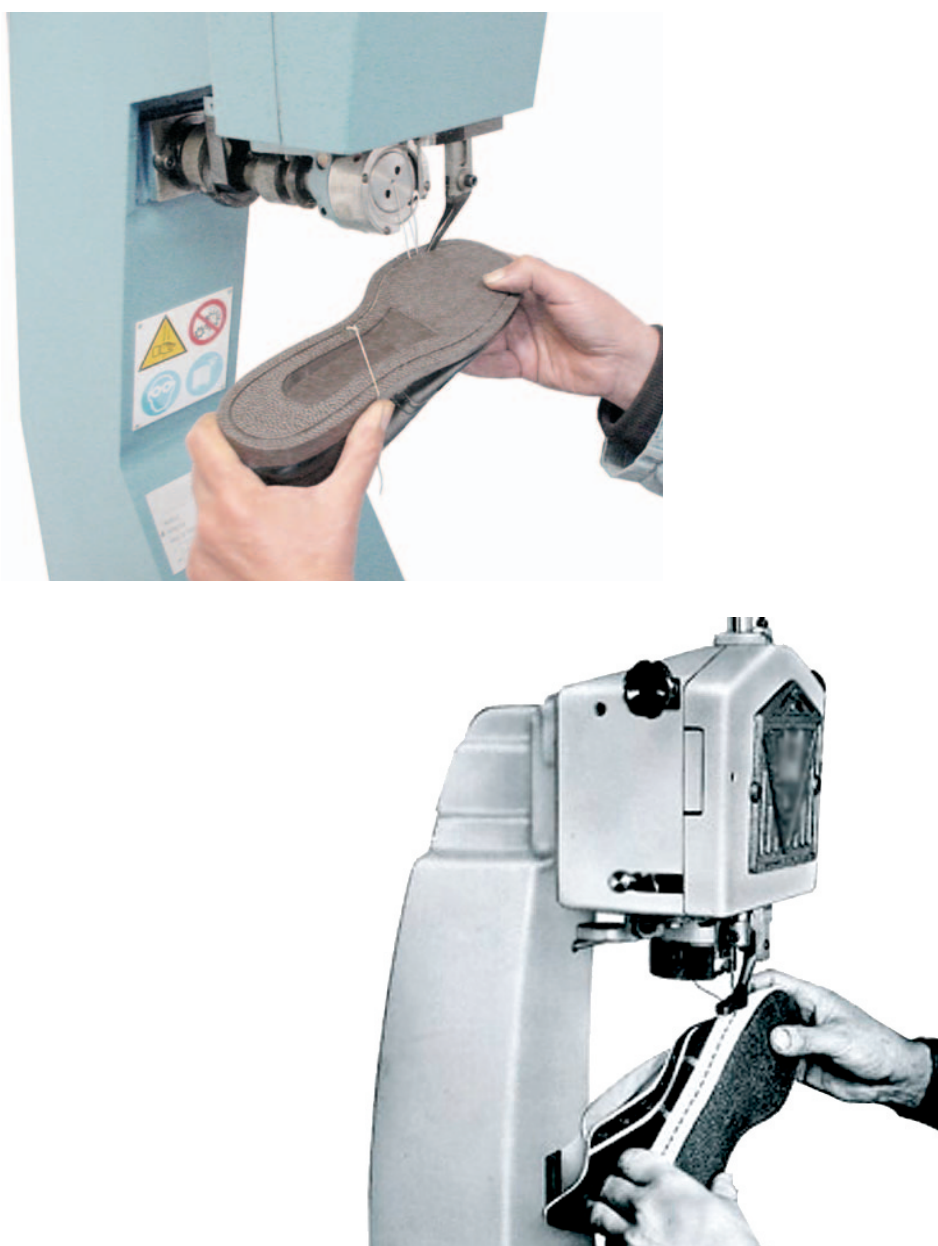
Exemple de machine pour la couture à Blake du fond de la chaussure sur la photo de gauche, et pour couture latérale de la semelle sur la photo de droite.
